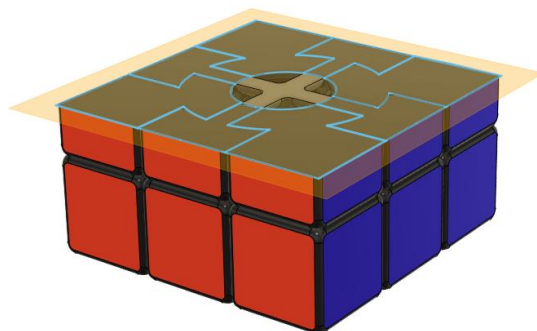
| Elaboración propia | Vista frontal del cubo con piezas remarcadas en azul
